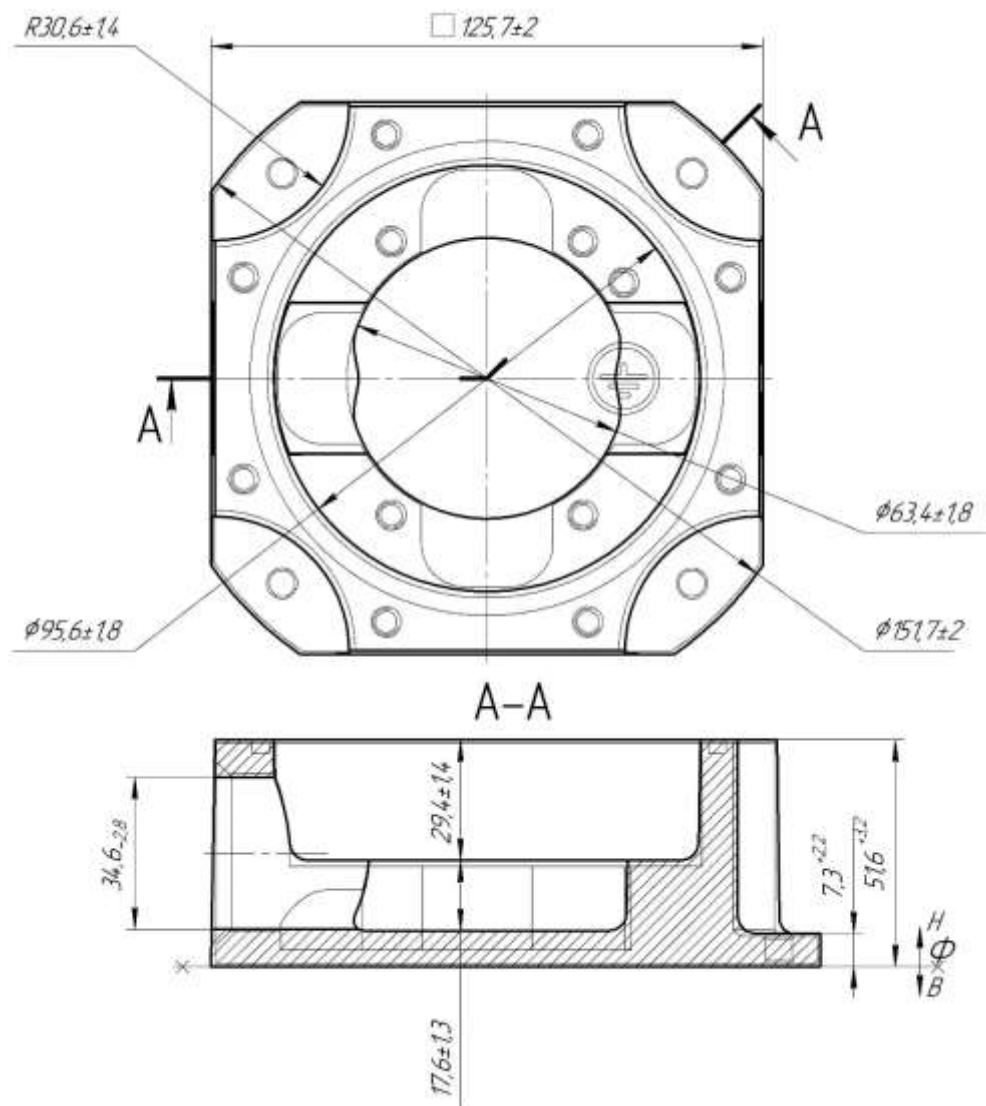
Заготованка для лиття за виплавлюваними моделями
